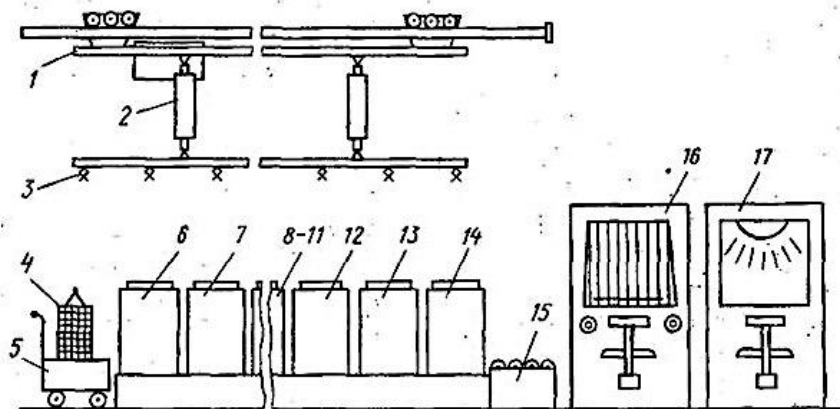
Схема автоматической установки для контроля деталей капиллярными методами [23]:
